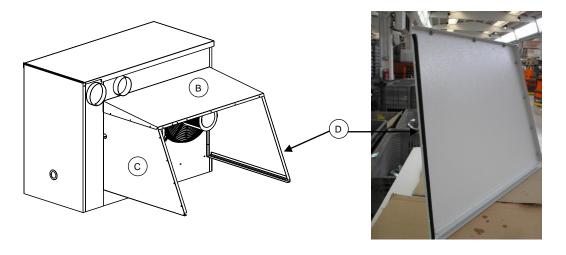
Размещение уплотнения и установка фланца воздухозаборного раструба
